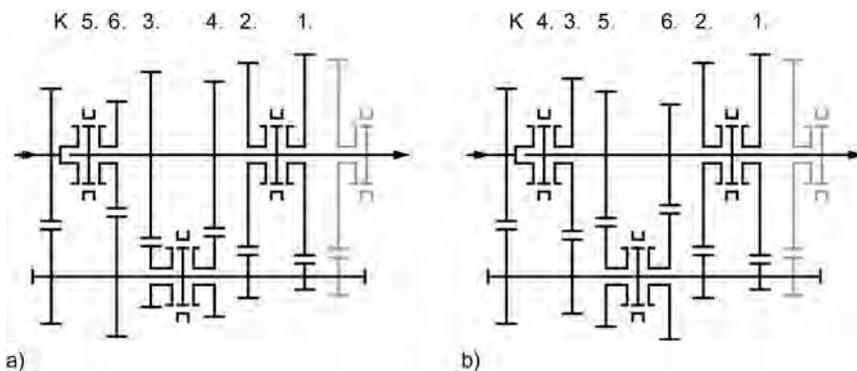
Zweistufiges 6-Gang-Getriebe (Getrag), ausgeführte Konstruktion Abb. 12.11. a Ausführung für Ottomotoren; b Ausführung für Dieselmotoren
